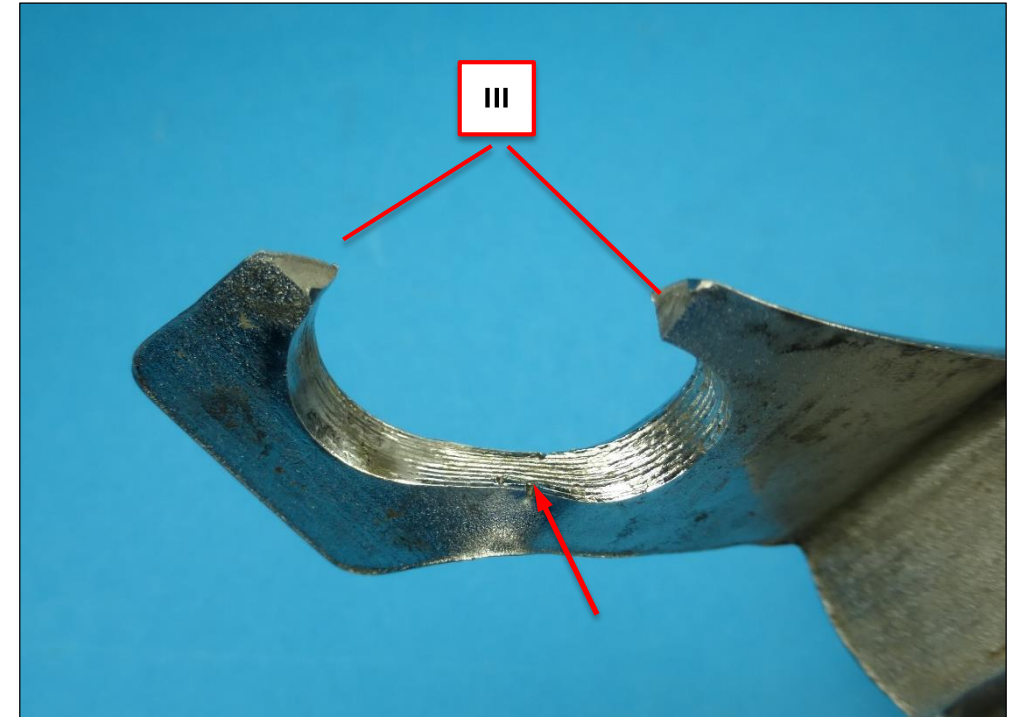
Detailaufnahme der Bruchstelle III, Pfeil kennzeichnet Anriss
